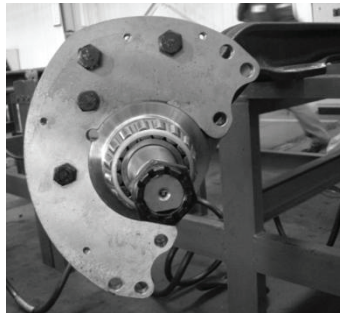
Разбрызгивание смазки, выходящей из подшипника ступицы переднего колеса
